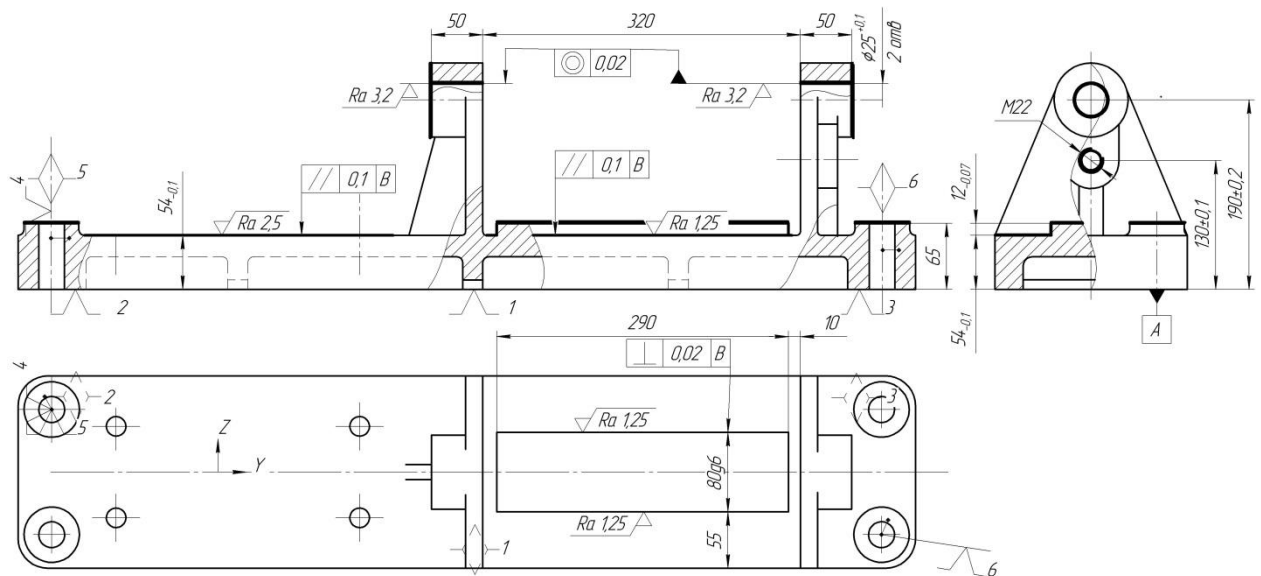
Базування заготовки при обробці на операції 010
